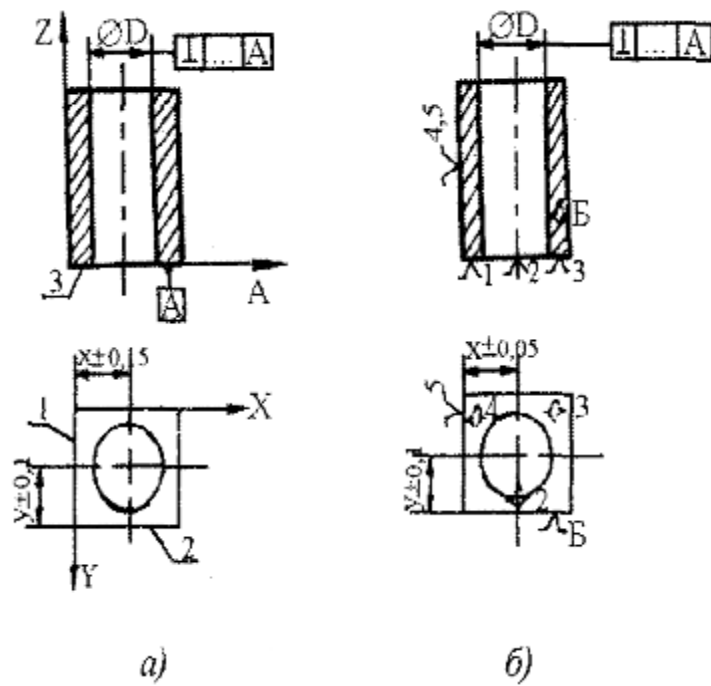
Координація отвору (а) і теоретична схема базування заготовки при його обробці (б)
